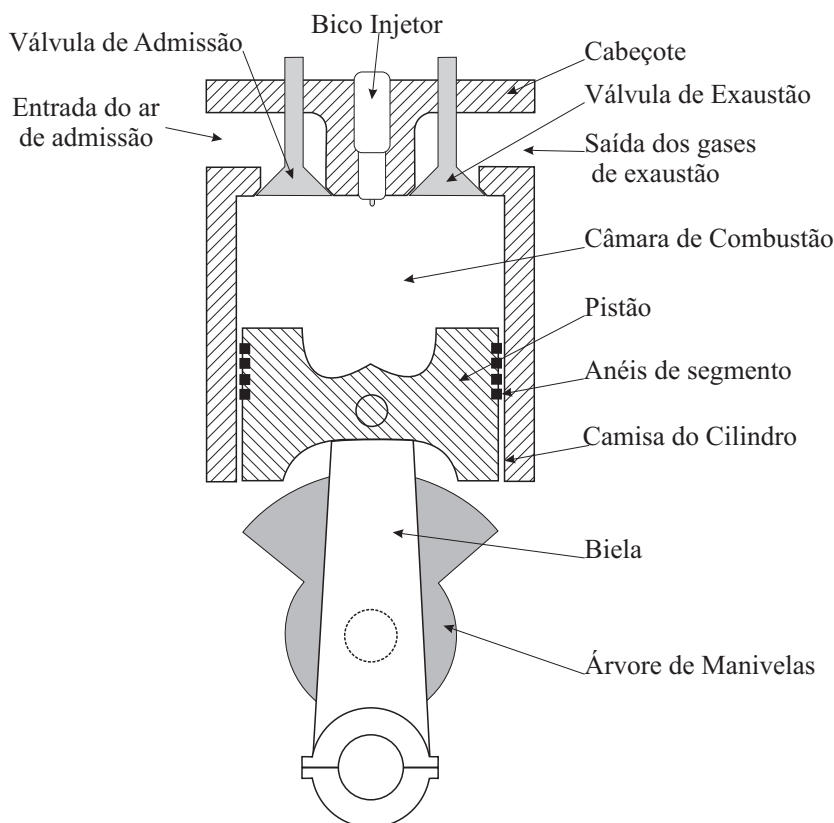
Partes componentes do cilindro de um motor diesel de quatro tempos.
